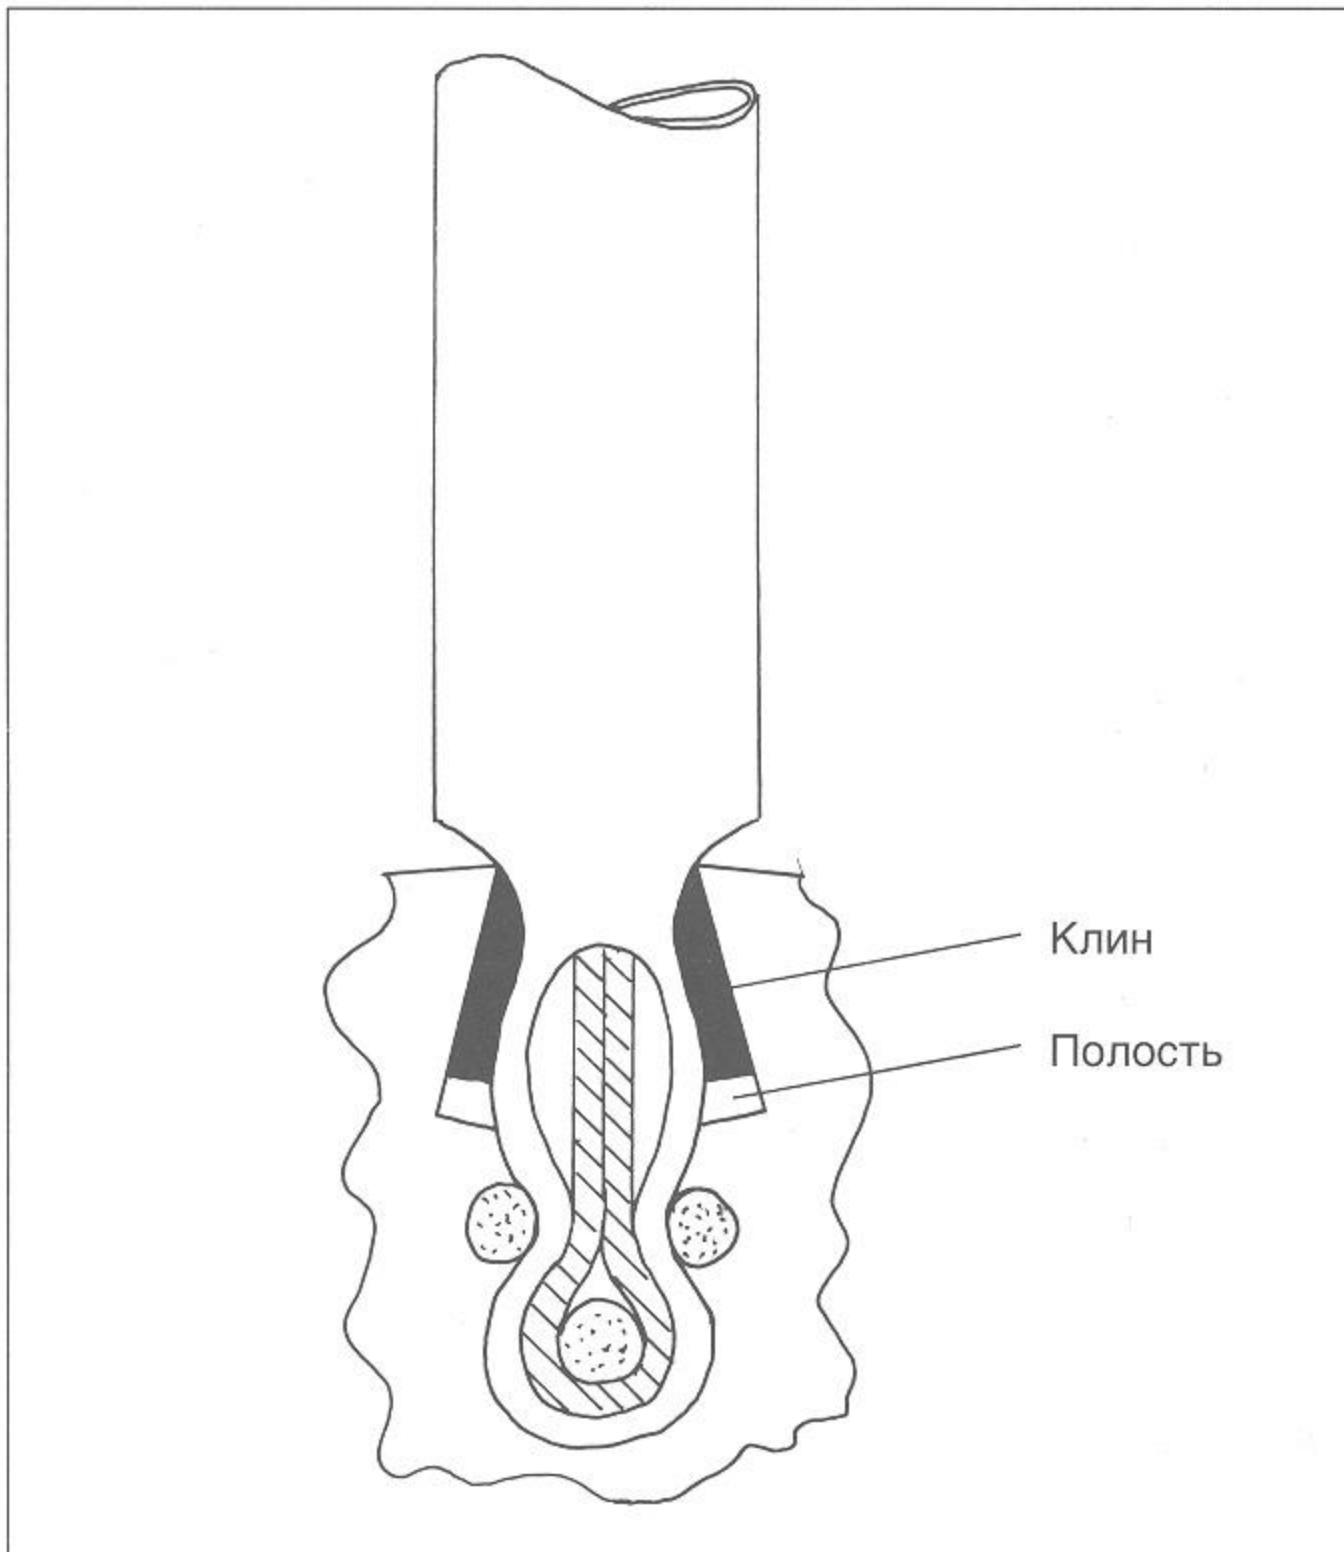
Доработанное крепление лопатки турбины двигателя БМВ 109-003 А-1
